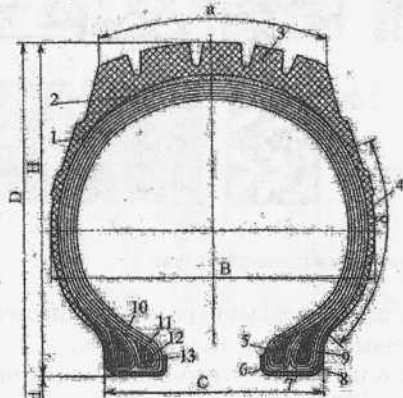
Основные части покрывки автотракторной шины: 1 – каркас; 2 – брекер; 3 – протектор; 4 – боковина; 5 – борт; 6 – пятка борта; 7 – основания борта; 8 – носок борта; 9 – бортовая лента; 10 – крыльевая лента; 11 – наполнительный шнур; 12 – обертка; 13 – бортовая проволока; В – ширина профиля; С – ширина раствора бортов; D – наружный диаметр; H – высота профиля; а – корона (беговая дорожка); б – боковина; d – посадочный диаметр
